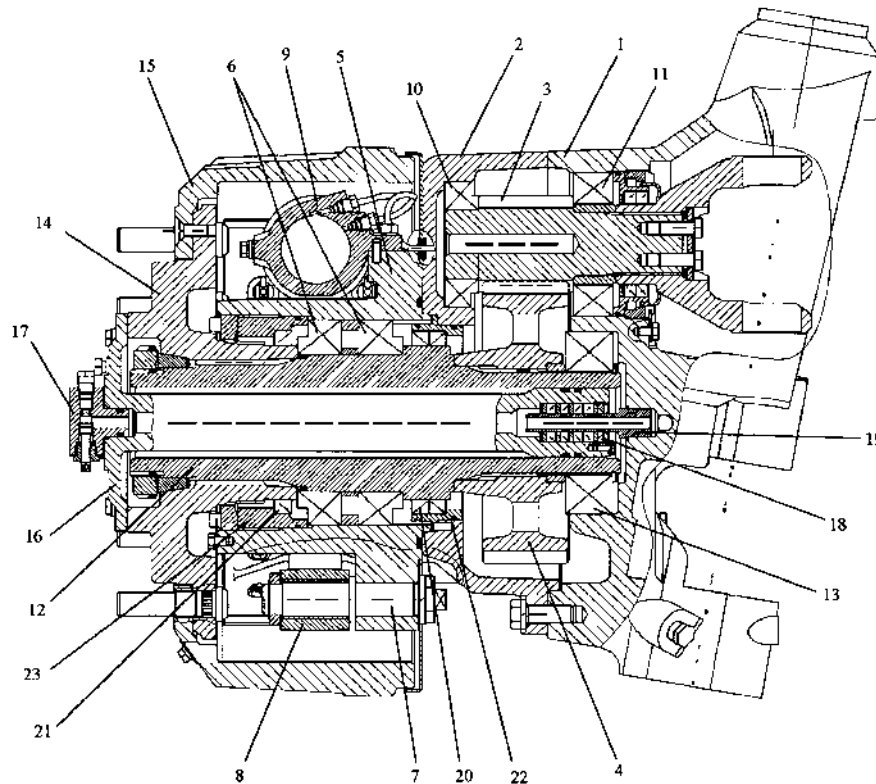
Конструкція редуктора в розрізі, де 1 - корпус колісного редуктора (картер); 2 - кришка корпусу; 3 - провідна циліндрична косозуба шестерня постійного зачеплення; 4 - ведена циліндрична косозуба шестерня постійного зачеплення; колодки колісного гальма, 9 - циліндр колісного гальма, 10 і 11 - конічні підшипники, 12 - вал колісного редуктора, 13 - підшипник, 14 - фланець колісного гальма, 15 - барабан колісного гальма, 16 - система накачування шин, 17 18 - блок ущільнення, 19 - трубка підведення повітря, 20, 21, 22 - манжети, 23 - захисний корпус.
